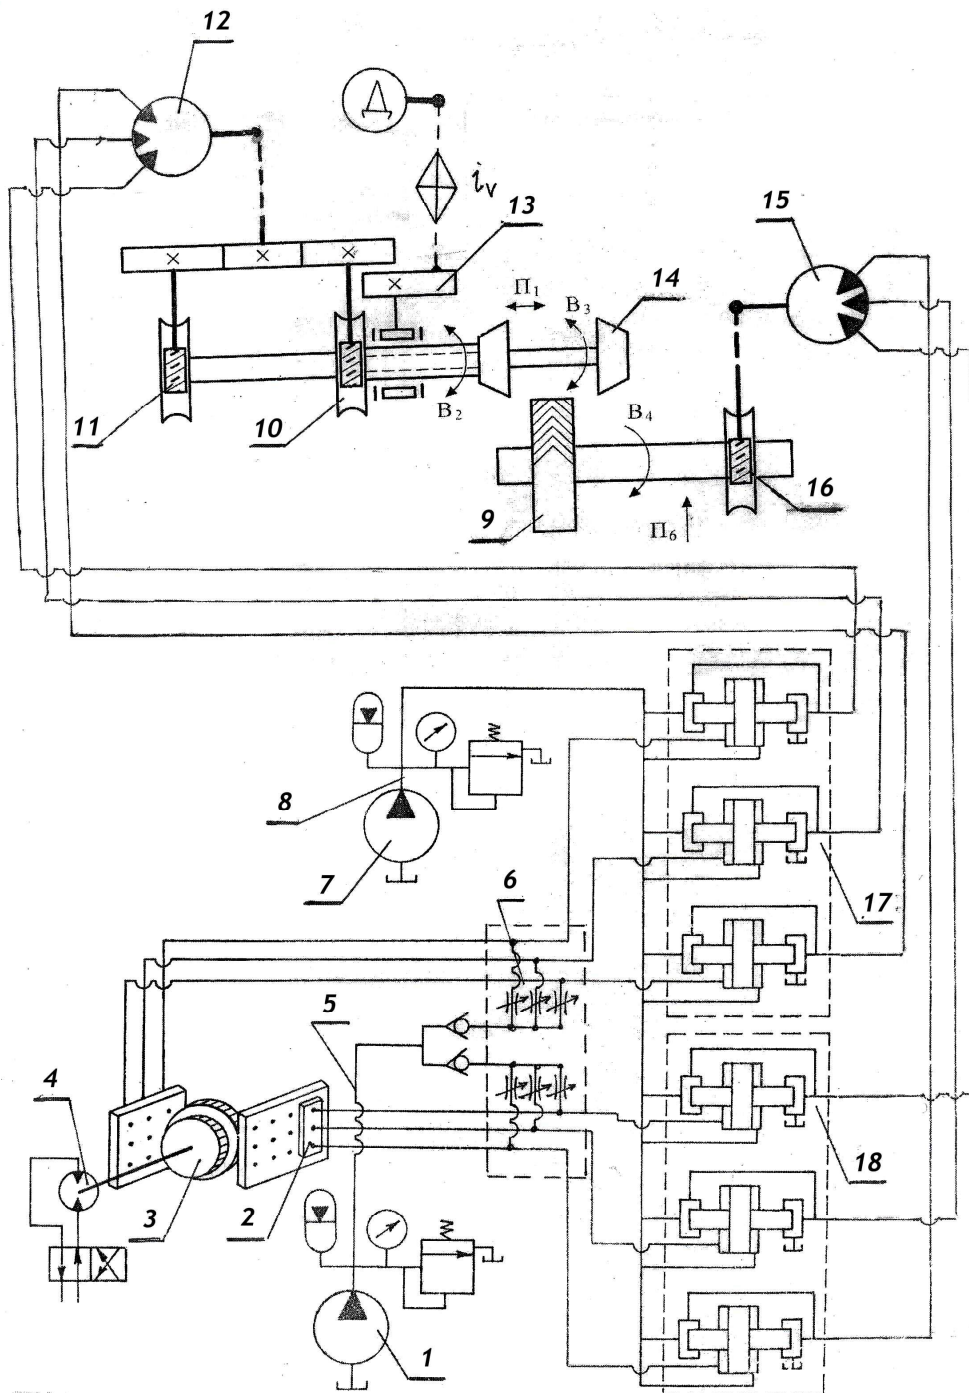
Структурная схема зубодолбежного станка с гидравлическими формообразующими связями для нарезания зубьев шевронных зубчатых колес двумя зуборезными долбьяками
